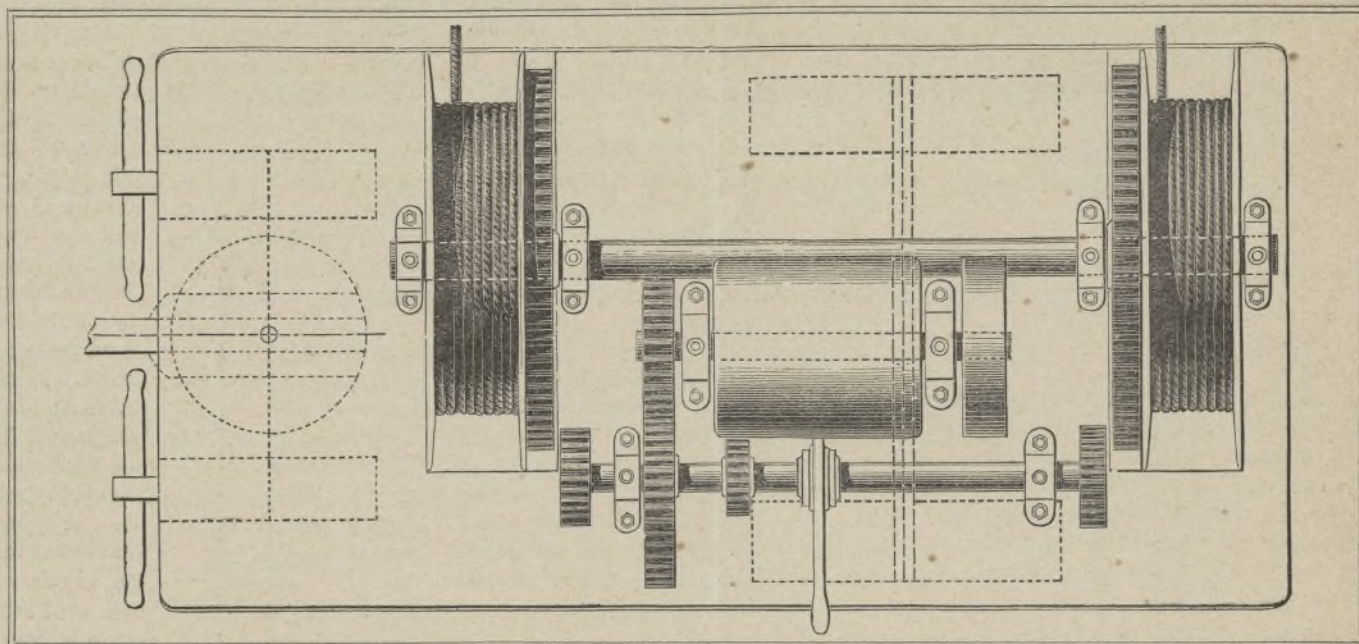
PLANIMETRIA DELL'ARGANO ELETTRO-DINAMICO.
